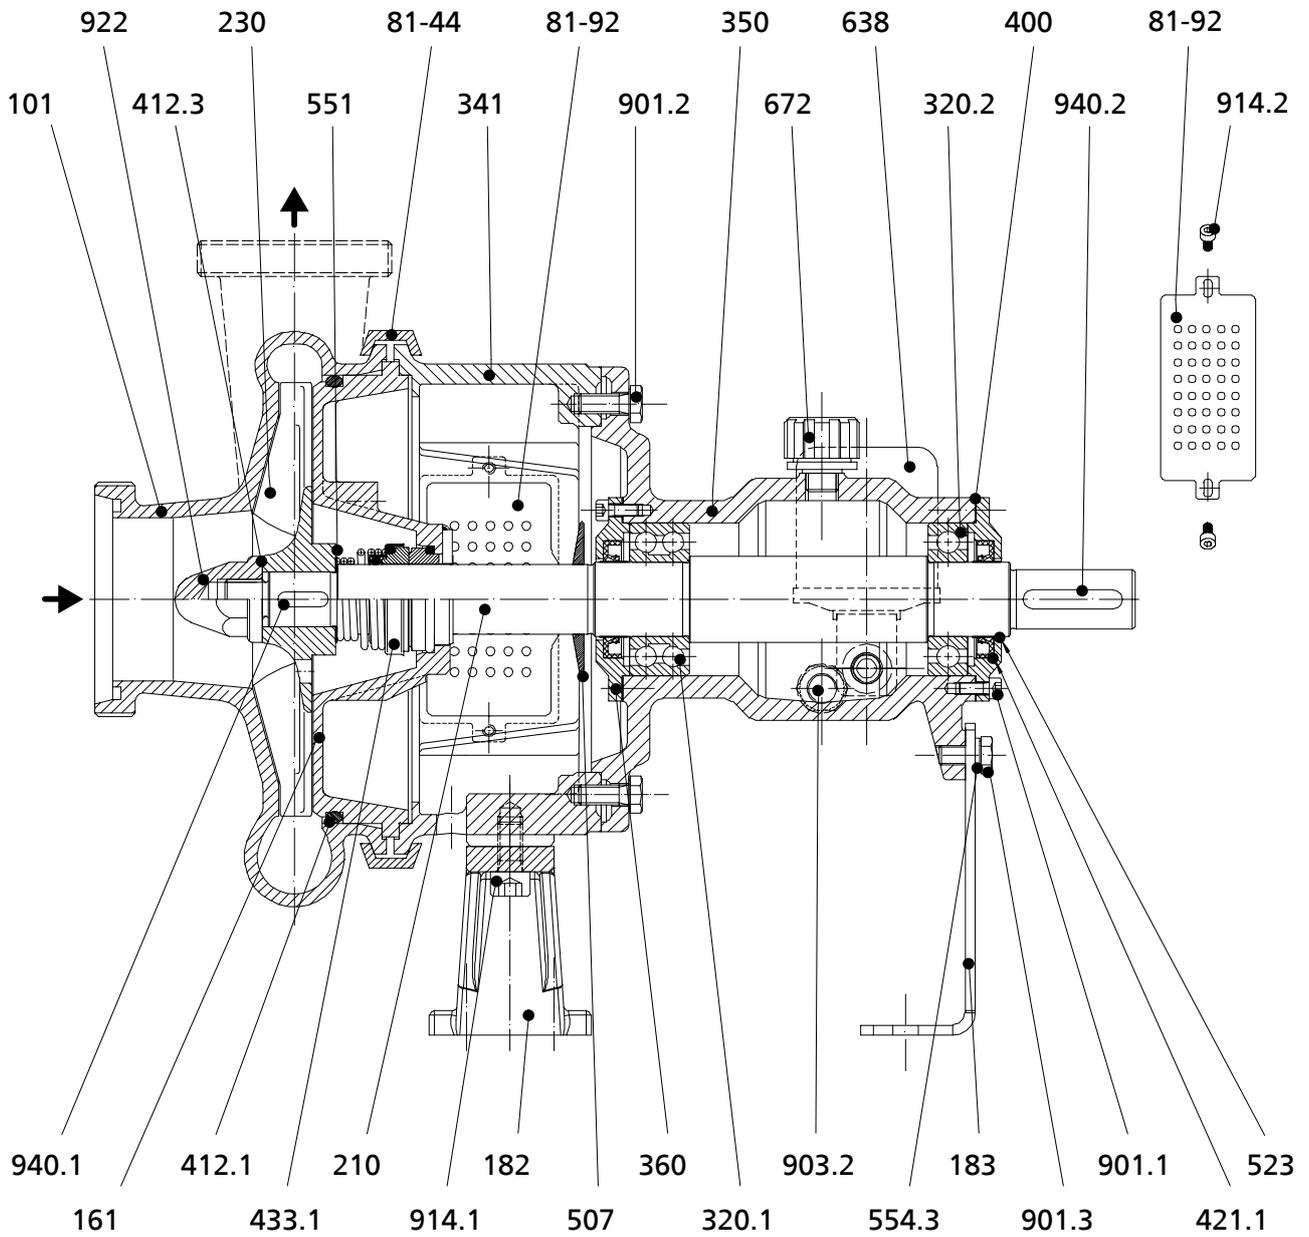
Gesamtzeichnung, Wellendurchmesser 28 mm, 43 mm
